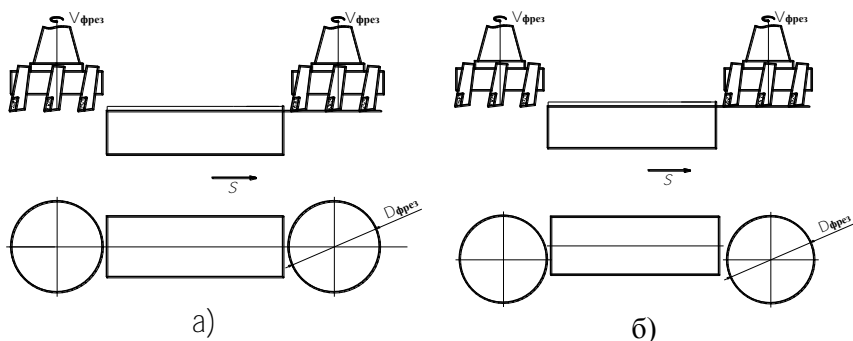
Схемы фрезерования: *а* – симметричное; *б* – несимметричное
